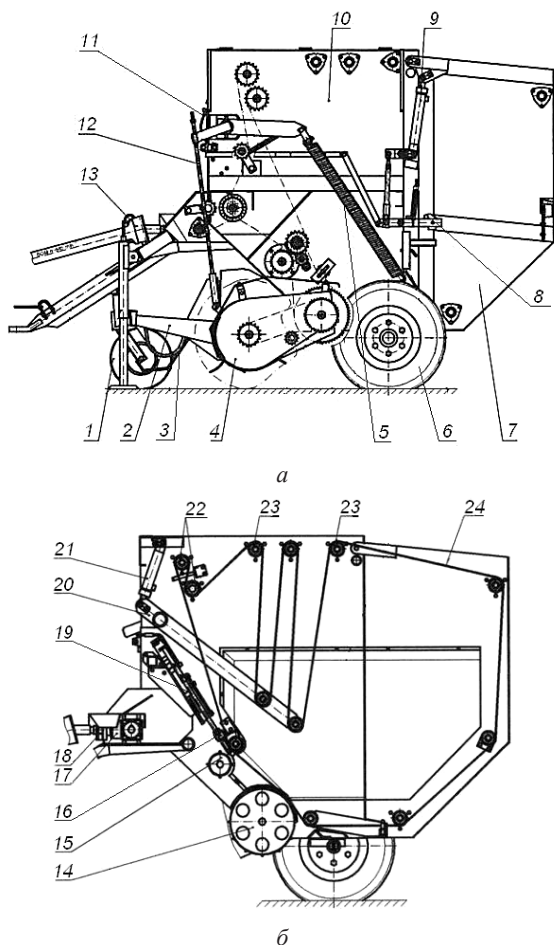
Общий вид (а) и прессовальная камера (б) пресс-подборщика лент льна: 1 – опорное колесо; 2 – копирующее устройство; 3 – прижимная решетка; 4 – подбирающий аппарат; 5 – пружина балансира; 6 – колесный ход; 7 – клапан прессовальной камеры; 8 – защелка; 9 – гидроцилиндр открытия клапана; 10 – прессовальная камера; 11 – шкала; 12 – тяга; 13 – карданный вал; 14 – питающий барабан; 15 – отбойный бите; 16 – аппарат обрезки; 17 – редуктор; 18 – предохранительная муфта; 19 – обматывающий аппарат; 20 – гидромеханический баланси; 21 – гидроцилиндр балансира; 22 – ведущие вальцы; 23 – ведомые вальцы; 24 – прессующие ленты
